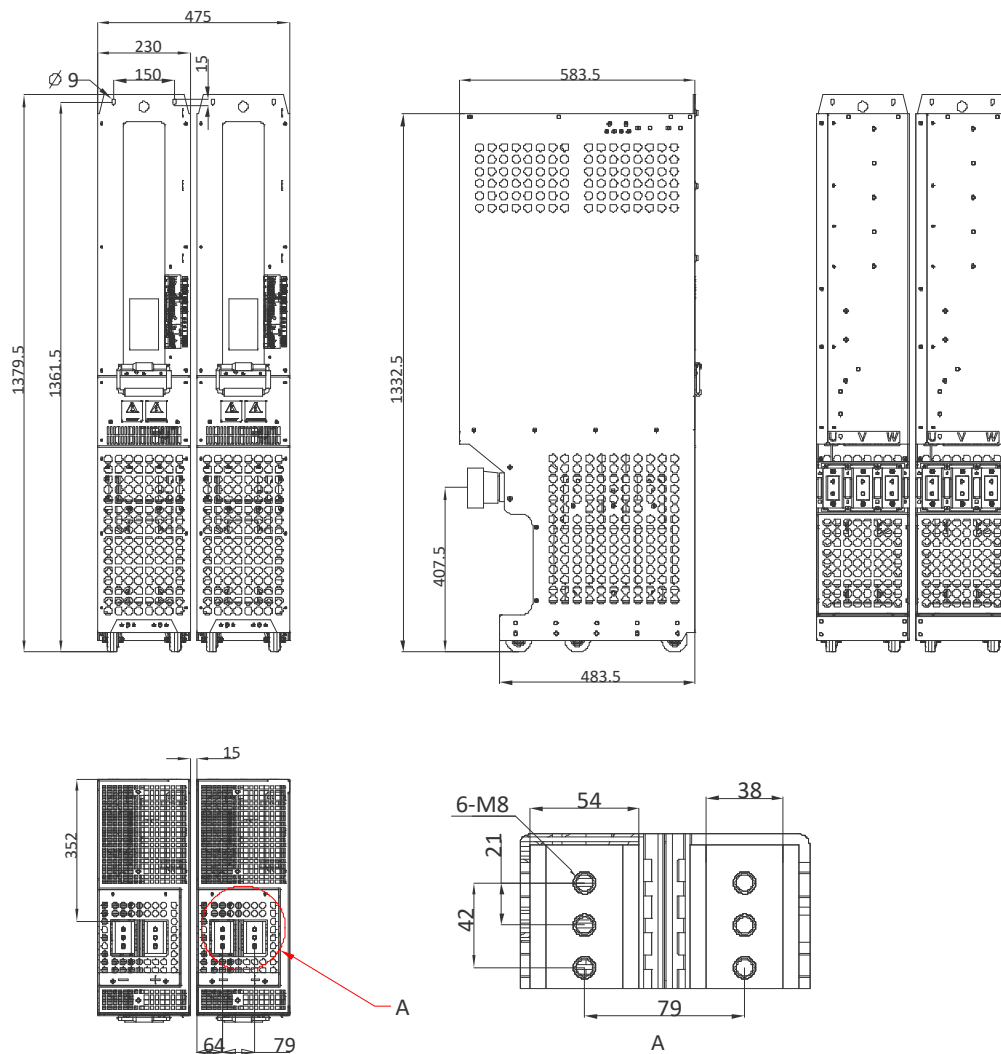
Габаритные размеры инвертора корпуса 2FR8 (мм)
